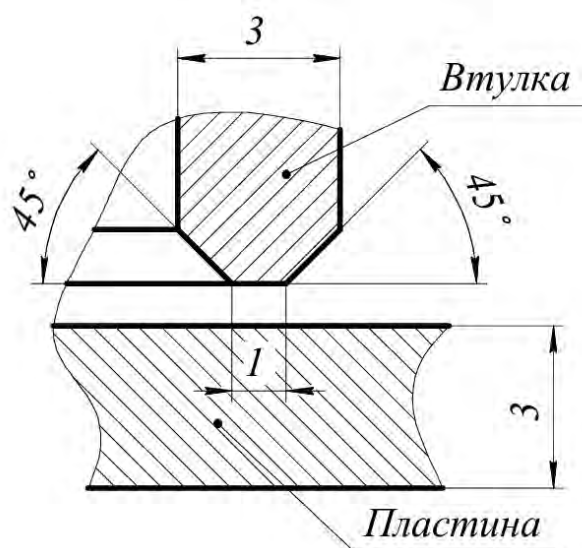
Трапецеидальная форма рельефа на торце втулки при контактной рельефной сварке втулки с пластиной
